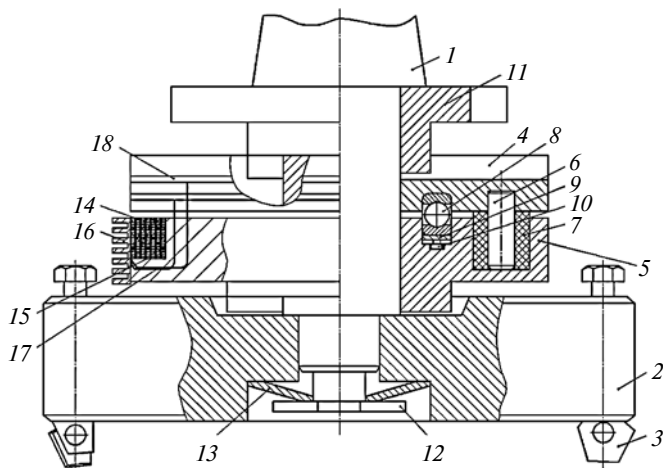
Сборная торцевая фреза с демпфирующими элементами: 1 — оправка; 2 — корпус; 3 — режущие пластины, 4 и 5 — верхнее и нижнее кольца узла демпфирования; 6 — штифт; 7 — демпфирующий элемент; 8 — стальные шарики; 9 — дистанционная шайба; 10 — упругая фигурная шайба; 11 — поводок; 12 — винт; 13 — пружинная шайба; 14, 15 — термоэлектрические модули Пельтье; 16 — радиаторы; 17 — изолированные провода; 18 — изолированный токопроводящий коллектор
